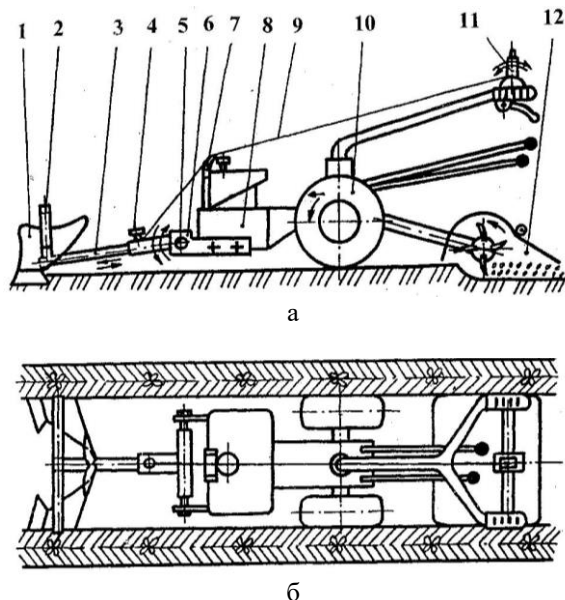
Стабілізуючий пристрій з робочим органом у вигляді передплужника: а – вигляд збоку; б – вигляд зверху; 1 – передплужники; 2 – штанга; 3 – телескопічний поводок; 4 – фіксатор; 5 – шарнір; 6 – кронштейни; 7 – направляючий щиток; 8 – рама мотоблока; 9 – трос; 10 – колеса мотоблока; 11 – рукоятки управління пристроєм; 12 – ґрунтова фреза
